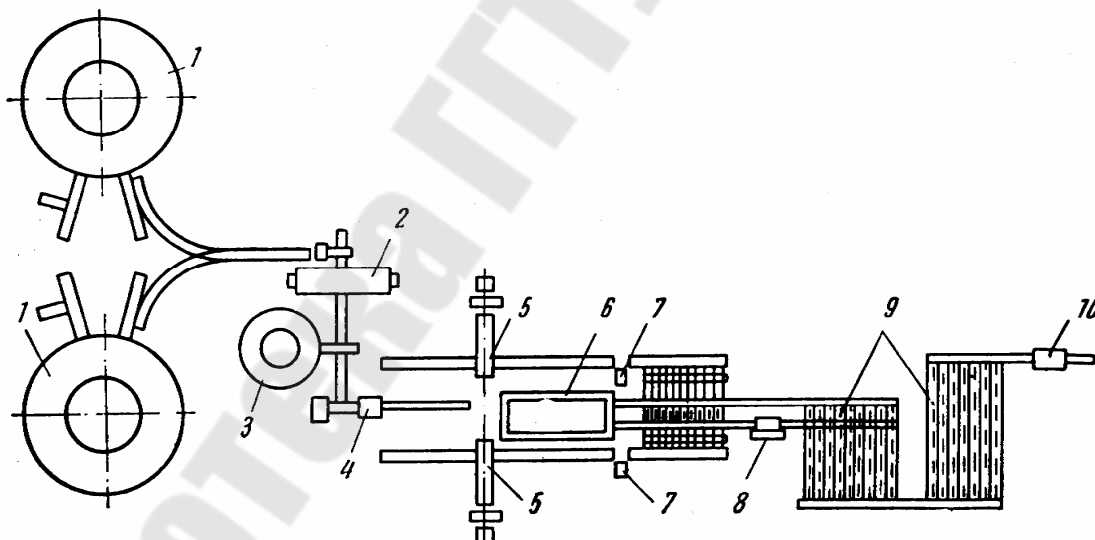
Расположение оборудования агрегата с двумя пилигримовыми станами: 1 – кольцевая печь; 2 – горизонтальный прошивной пресс; 3 – кольцевая подогревательная печь; 4 – стан-элонгатор; 5 – пилигримовый стан; 6 – подогревательная печь; 7 – пила; 8 – калибровочный стан; 9 – охлаждающий стол; 10 – правильный стан
